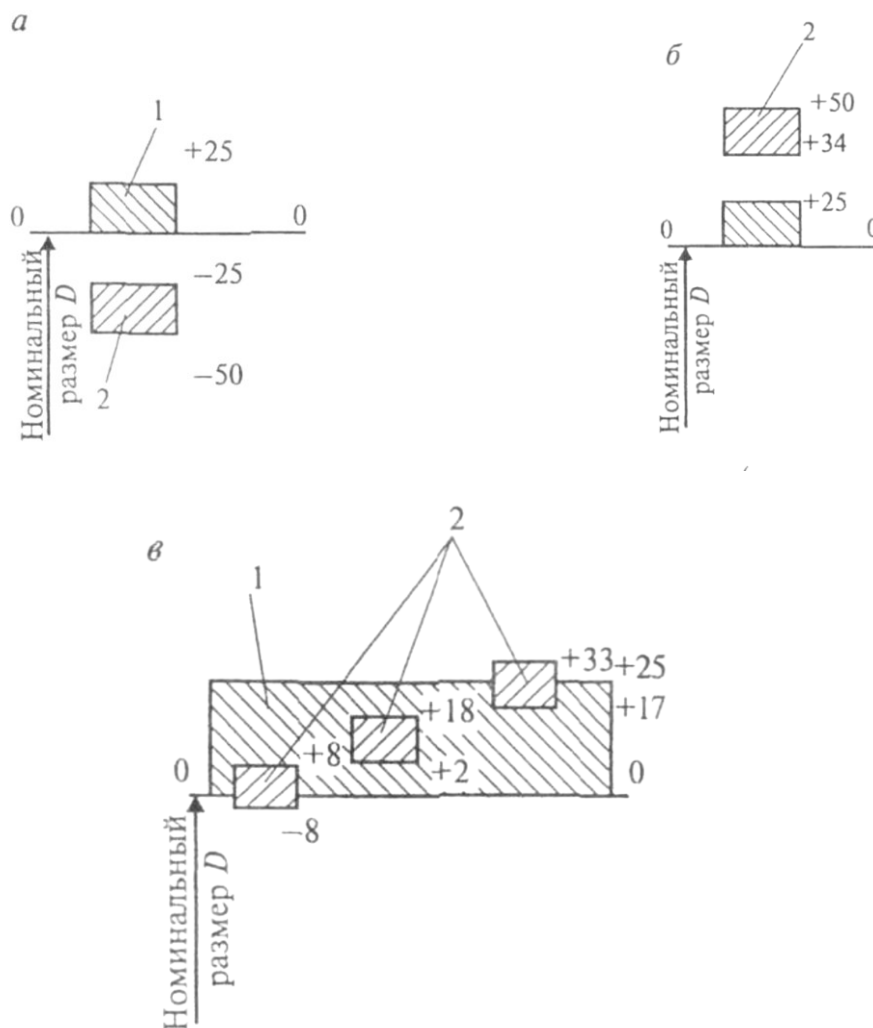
Схемы полей допусков (отверстия – 1 и вала - 2) для разных посадок: а – зазор; б – натяг; в – переходная посадка.
